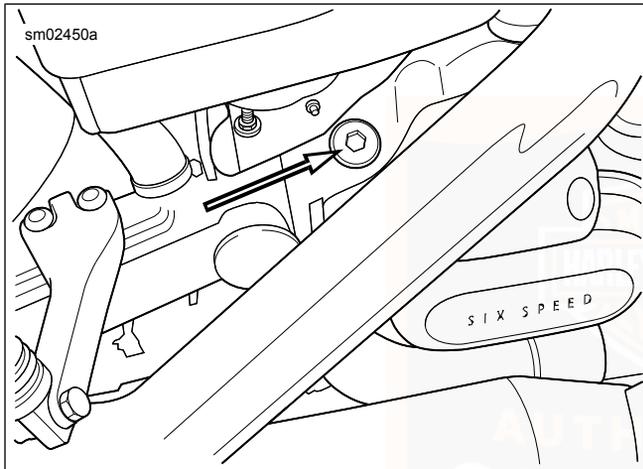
Lage des Getriebeeinfüllverschlussstopfens/Ölmesstabs
